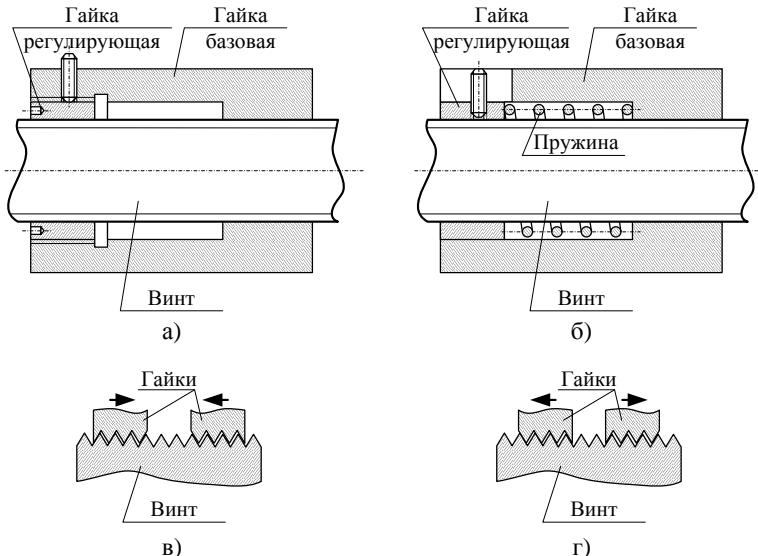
Схема люфтовыбирающего механизма на основе гайки с жесткой и упругой регулировкой осевого зазора
